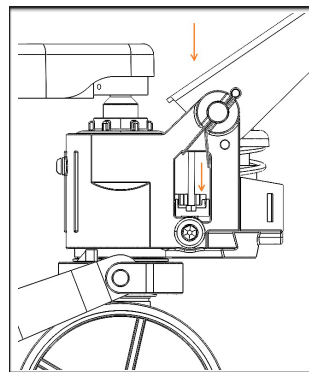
Colocar o eixo de conexão; Inserte el pasador; Insérez le goupille; Setzen Sie den Stift ein; Insert the connecting shaft.
